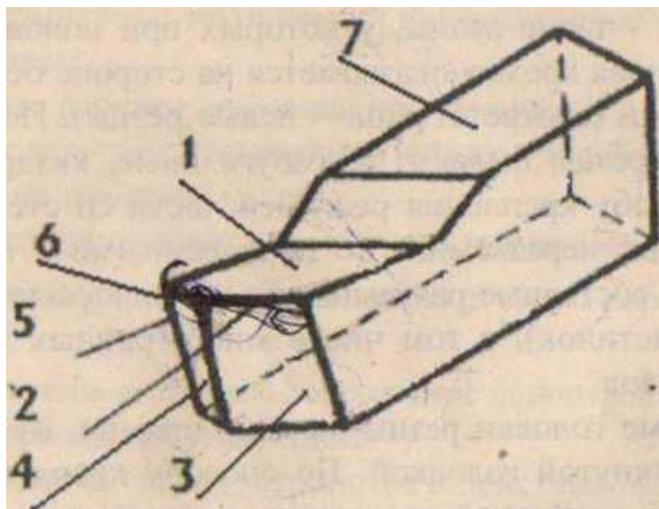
Элементы резца : 1- передняя часть; 2 - главная режущая часть; 3 - главная задняя поверхность; 4 - вспомогательная задняя поверхность; 5 - вершина резца; 6 - вспомогательная режущая кромка; 7 - тело резца
